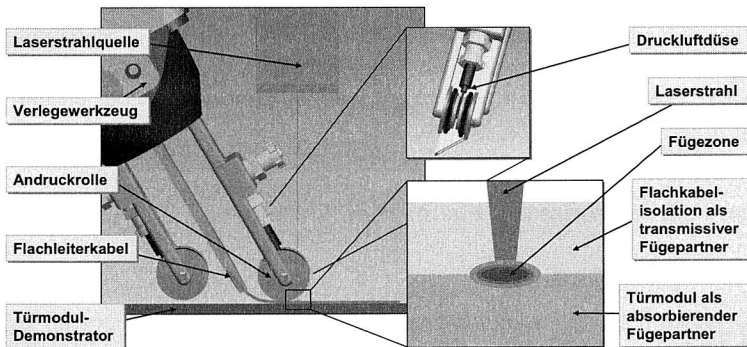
Integration eines Laserstrahlschweißprozesses in das dritte prototypische Verlegewerkzeug für Flachleiterkabel
